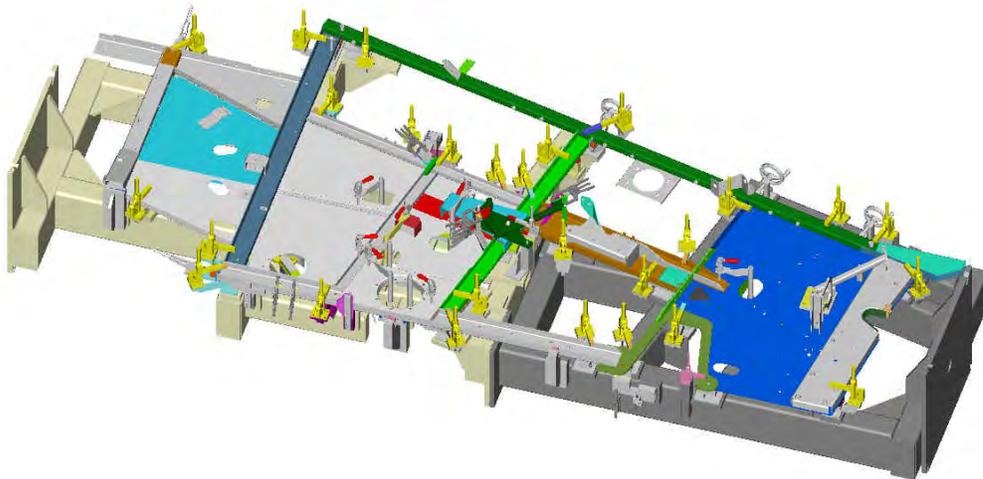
MONTAGEM VIRTUAL DE UMA FERRAMENTA DE FIXAÇÃO PARA SOLDA
